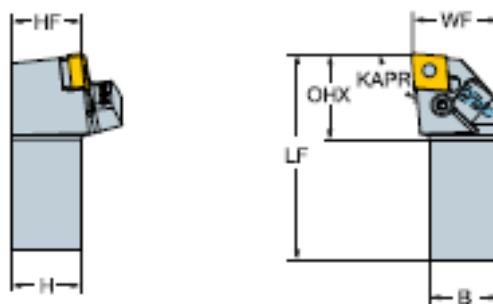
Державка для наружного точения PCLNR 2525M 12HP
